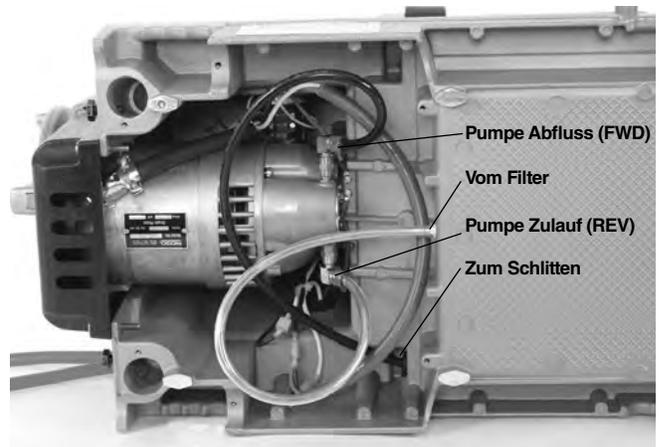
B – Ölpumpenanschlüsse für das Schneiden von Rechtsgewinden (Schalter auf FWD)
